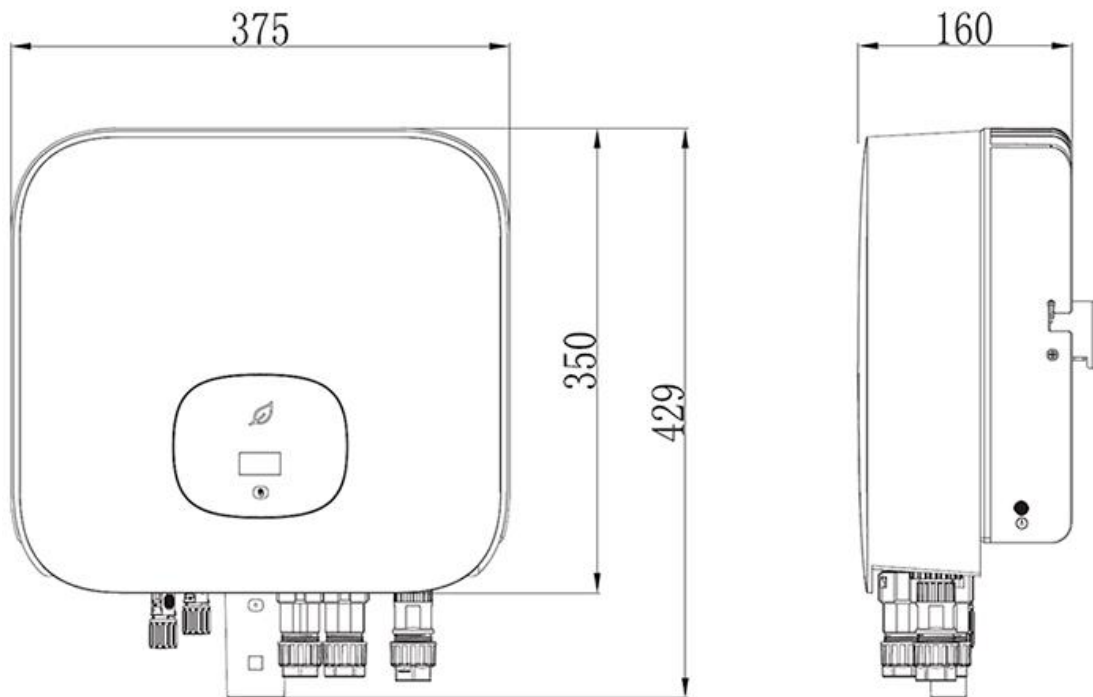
Dimensiones del inversor (Fuente: fabricante)
